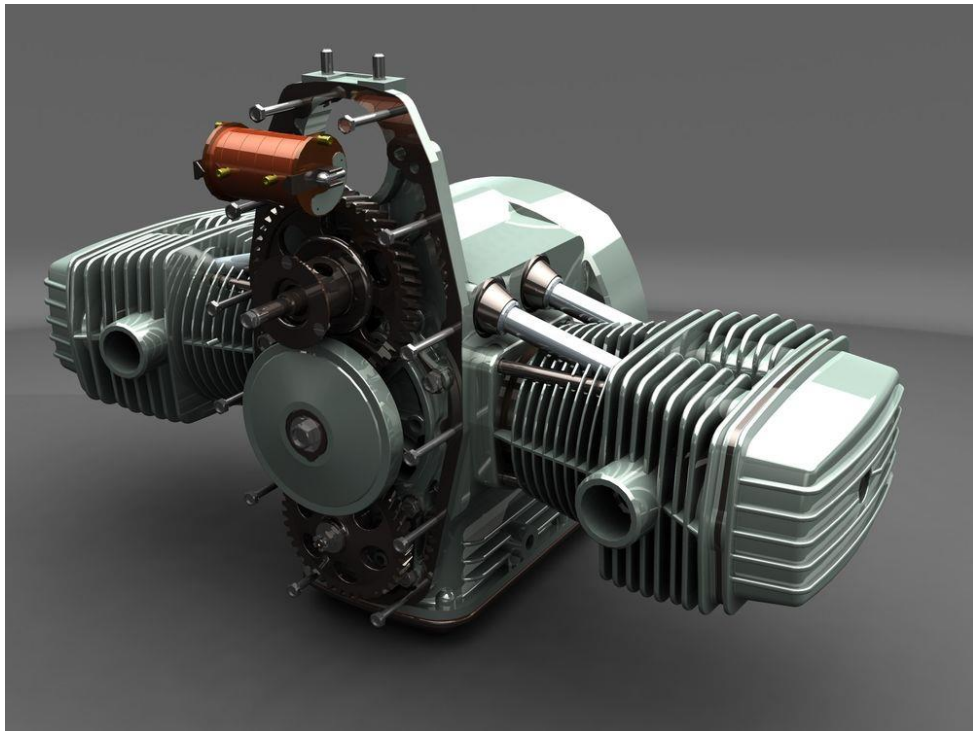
Біметалевий циліндр двигуна «К-650» [19]
